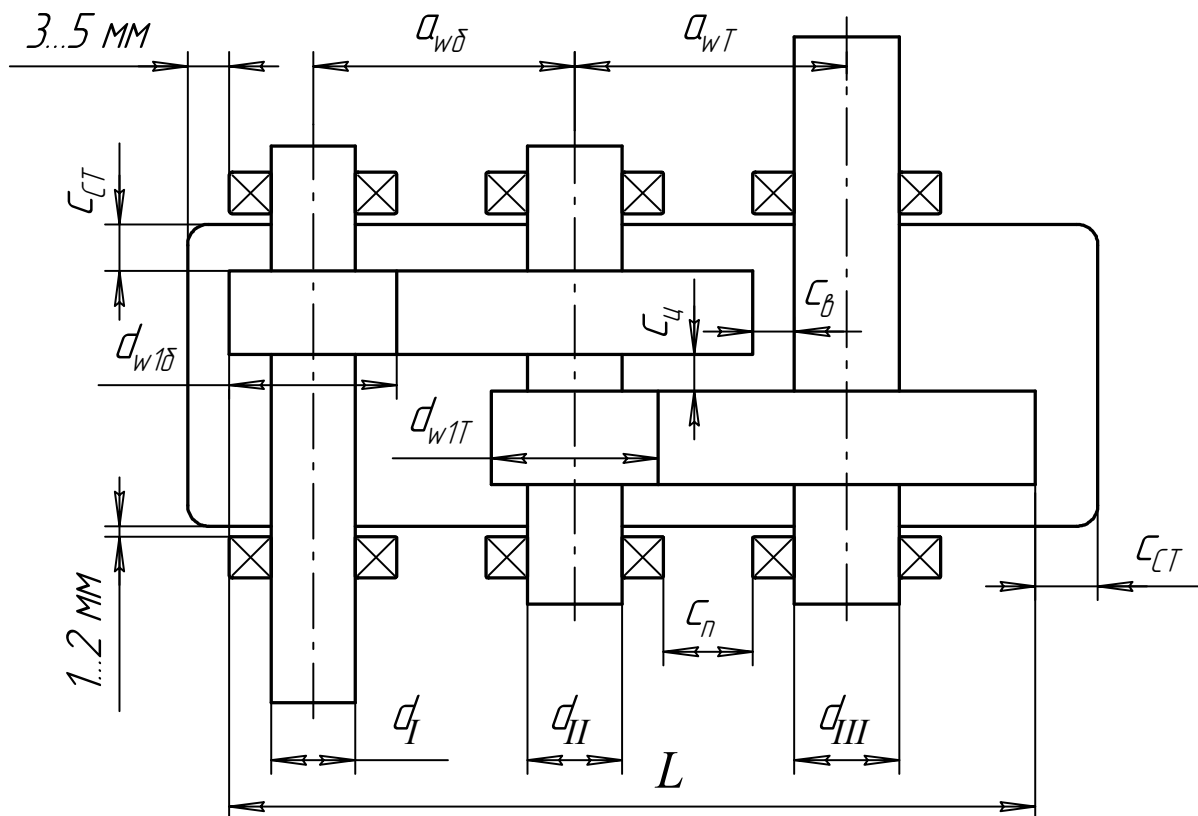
Расположение колёс и подшипников двухступенчатого цилиндрического редуктора
